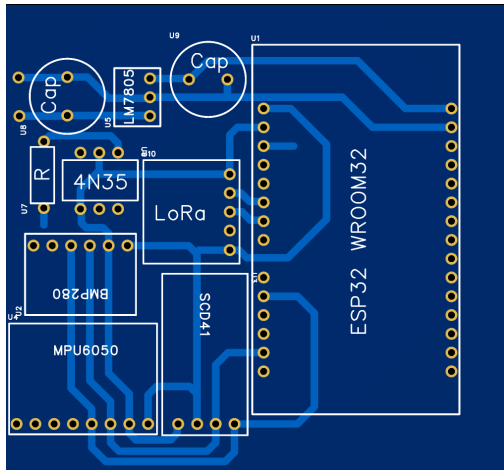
Vista previa del diseño final de PCB transmisor en modo producción.
